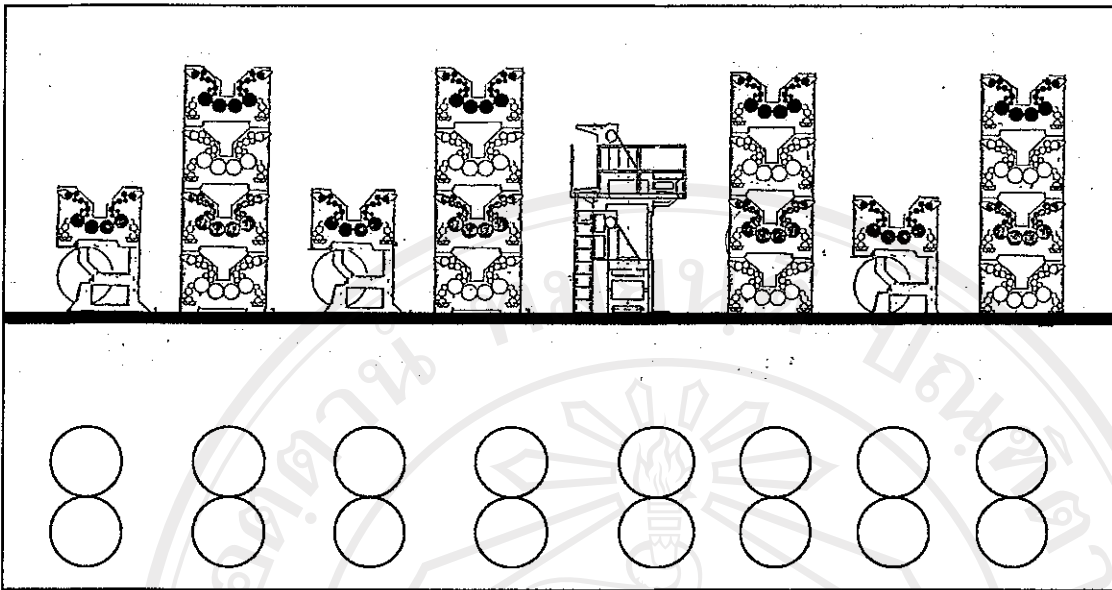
แสดงถึง PLATE และ BLANKET CYLINDER
